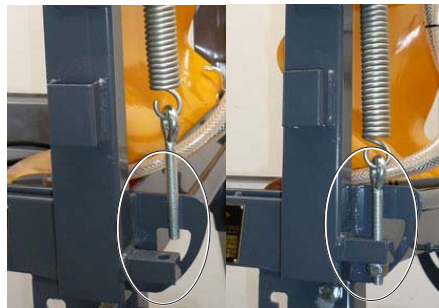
, Стопорная пружина качающегося режущего рычага с рым-болтом, шайбой гайкой закрепляется на раме CTS • 175.1
